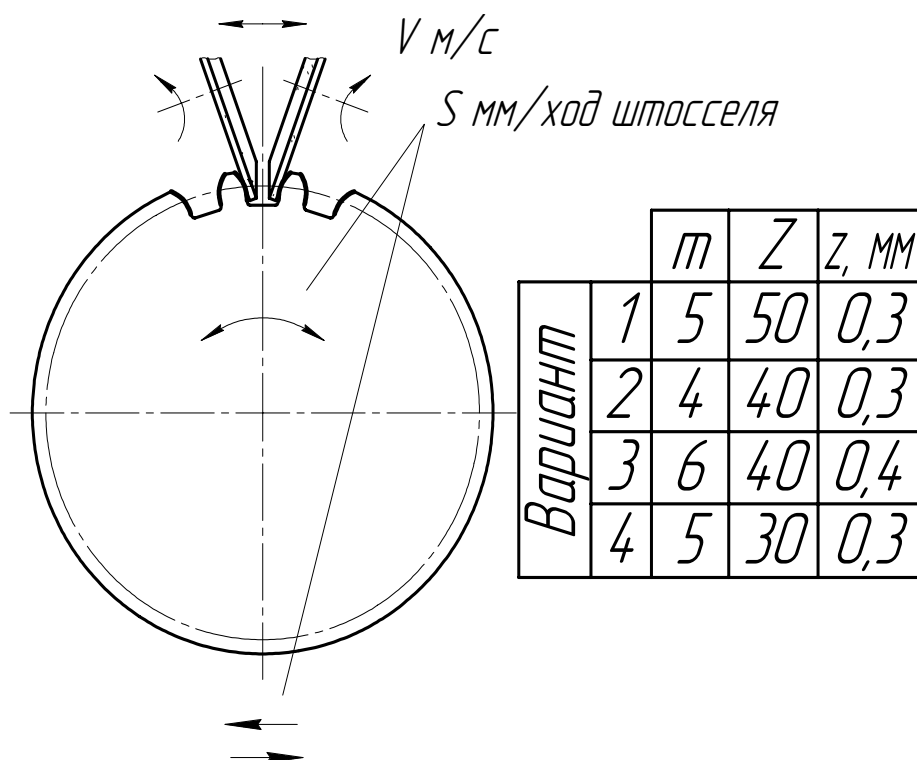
Шлифование зубчатых колес тарельчатыми кругами (z – припуск, мм, B – высота зубьев 30 мм)
